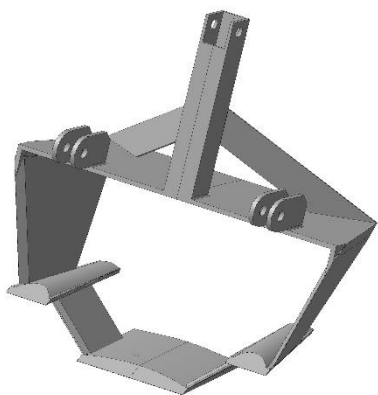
Глубокорыхлитель с криволинейной поверхностью режущей части.
